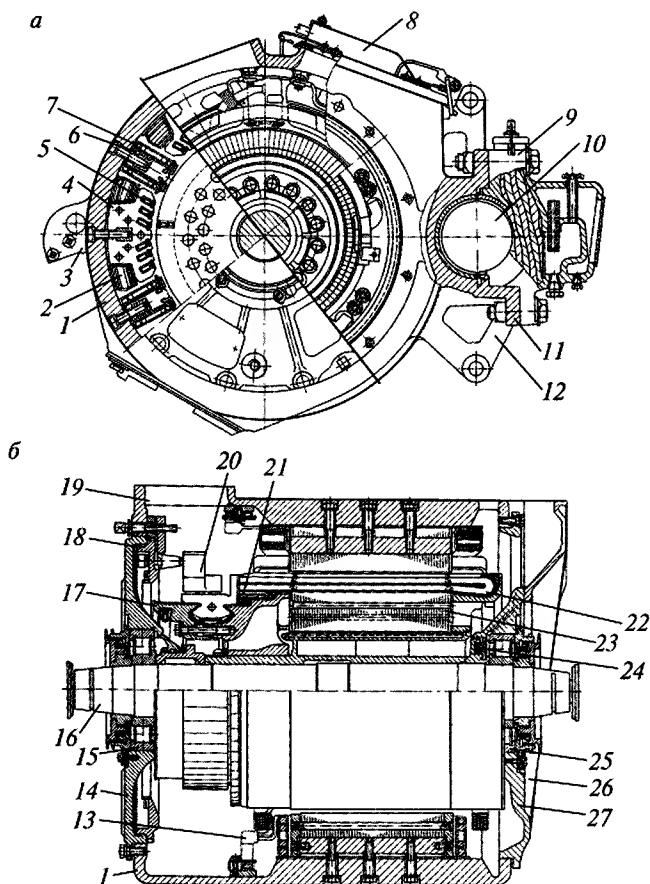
Поперечный (а) и продольный (б) разрез тягового электродвигателя НБ-418К6:
